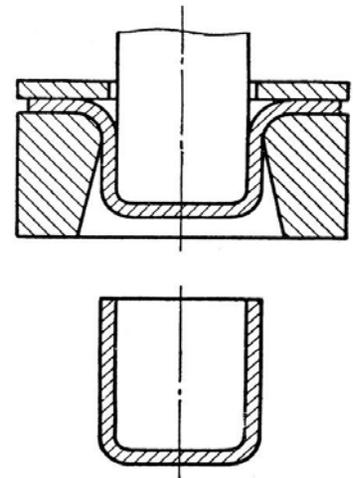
Схема процесса вытяжки и готовая деталь
